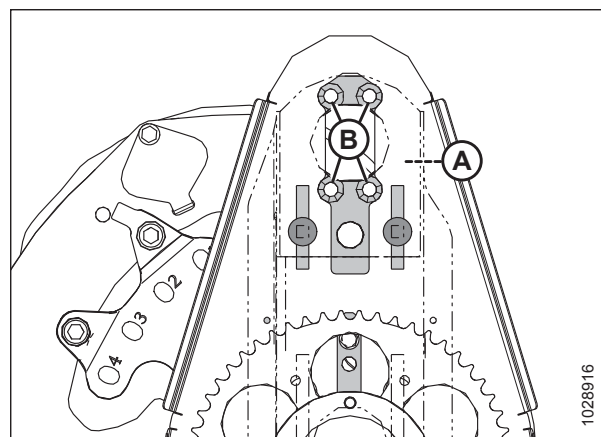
Befestigungsbohrungen des Haspelantriebsmotors
